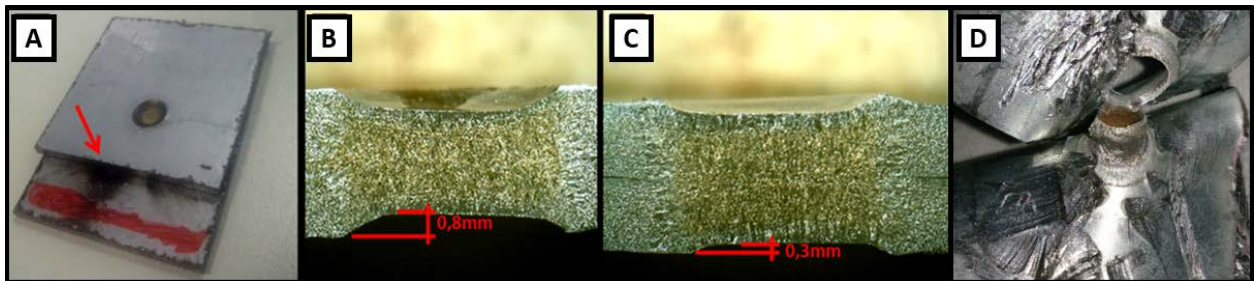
(a) Expulsão de material entre chapas; (b) Macrografia da seção transversal -10x de aumento - indentação alta; (c) Macrografia apresentando ponto de solda OK; (d) Teste de arrancamento apresentando ponto de solda OK.
